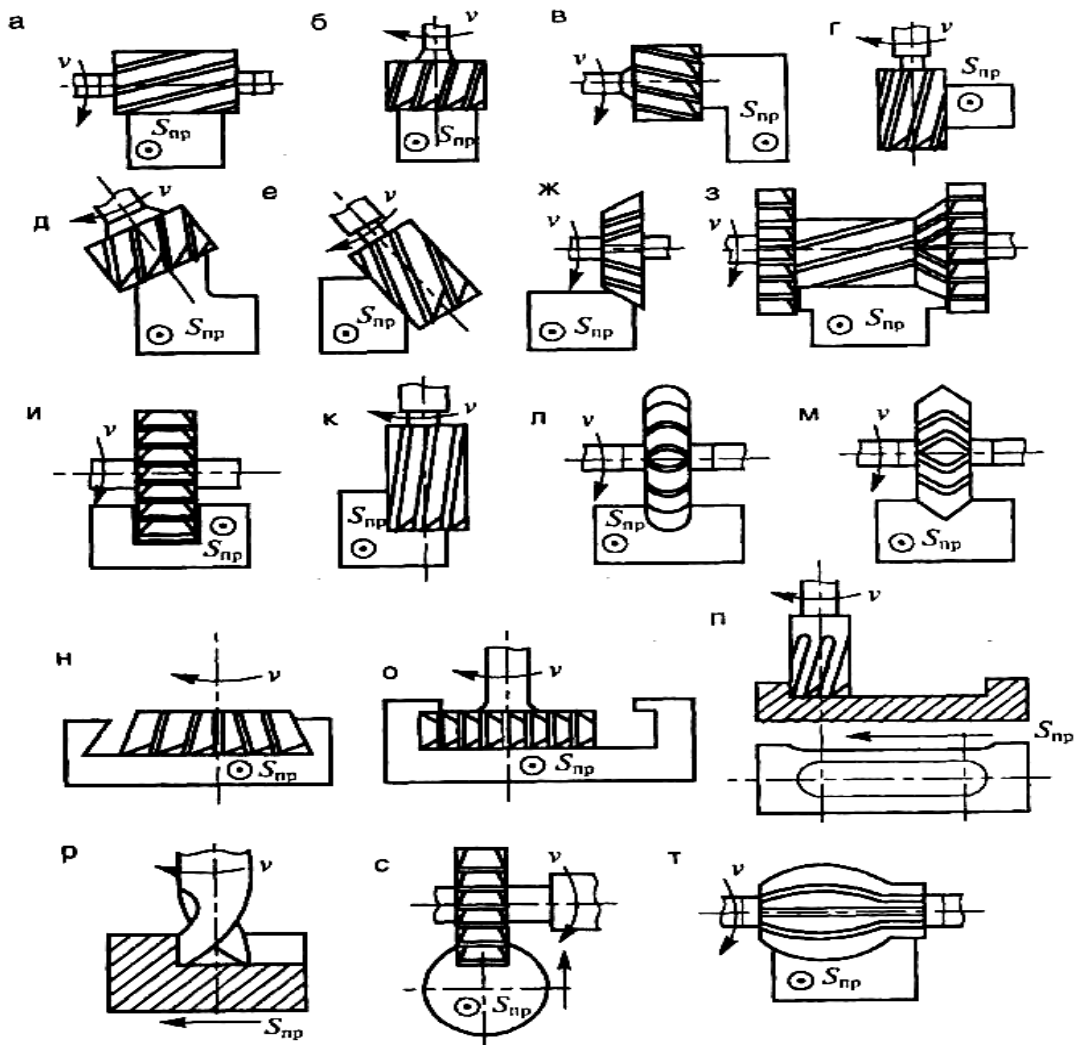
Виды фрез и схемы обработки фрезерованием
